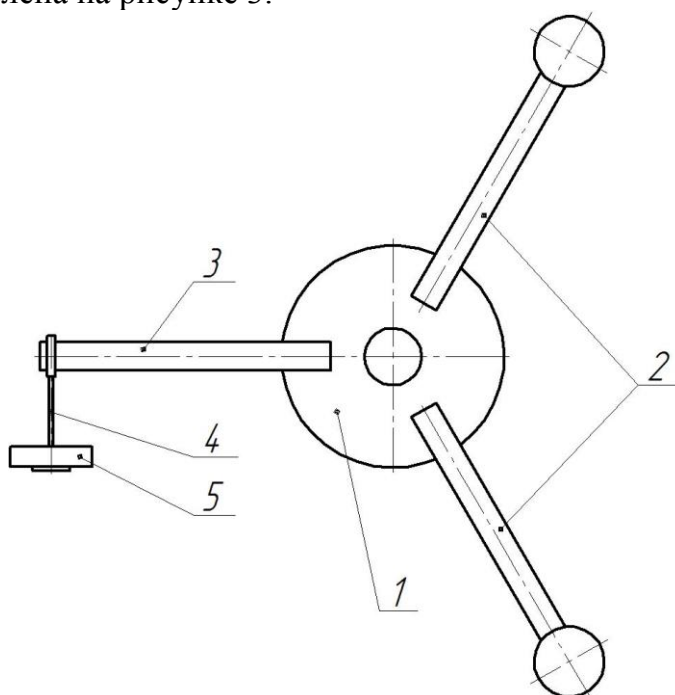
Схема нагружающего устройства: 1 – вал шестерня; 2 – ручка перемещения пиноли; 3 – стержень нагружающего устройства; 4 – подвесная система; 5 – груз
